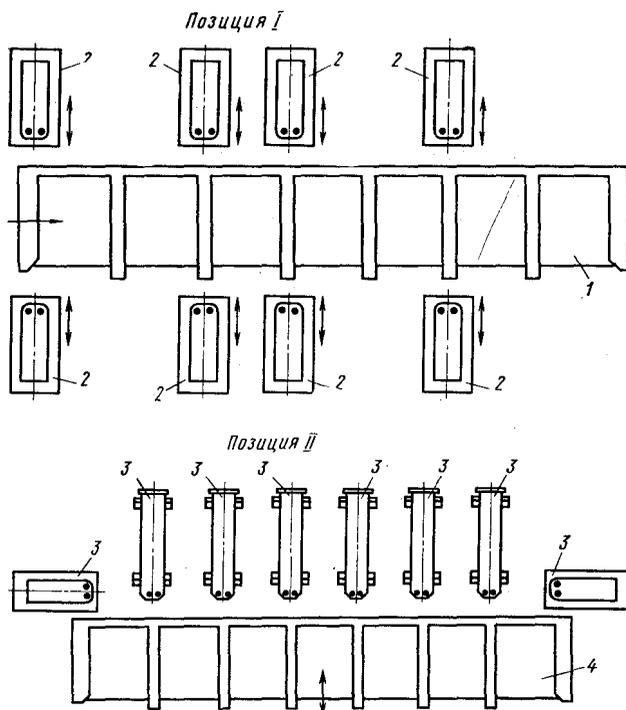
Схема расположения контактных точечных машин линии сварки каркаса боковой стенки с обшивкой
